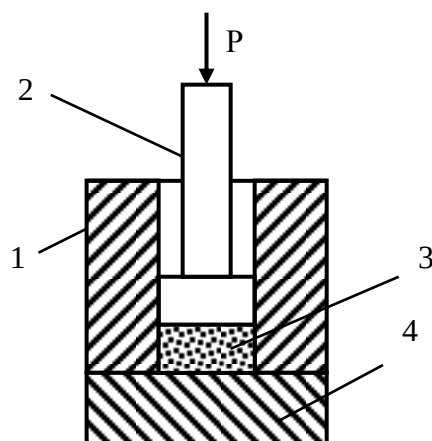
Схема прес-форми для пресування циліндричних заготовок: 1 – матриця; 2 – пуансон; 3 – металевий порошок; 4 – піддон.
